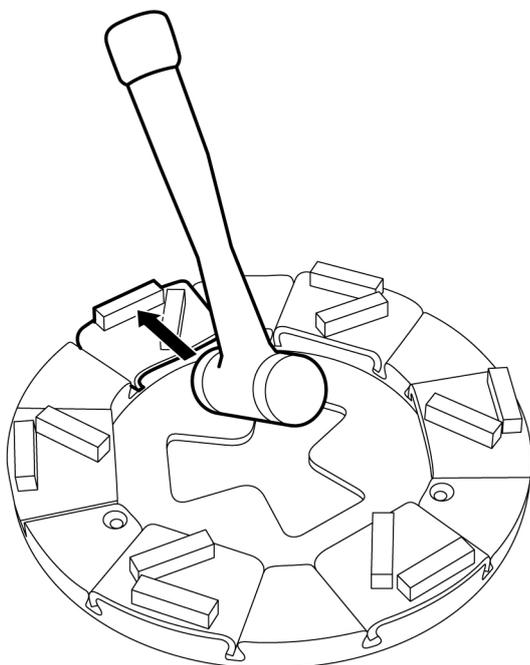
Verriegeln eines Schleifwerkzeugs
